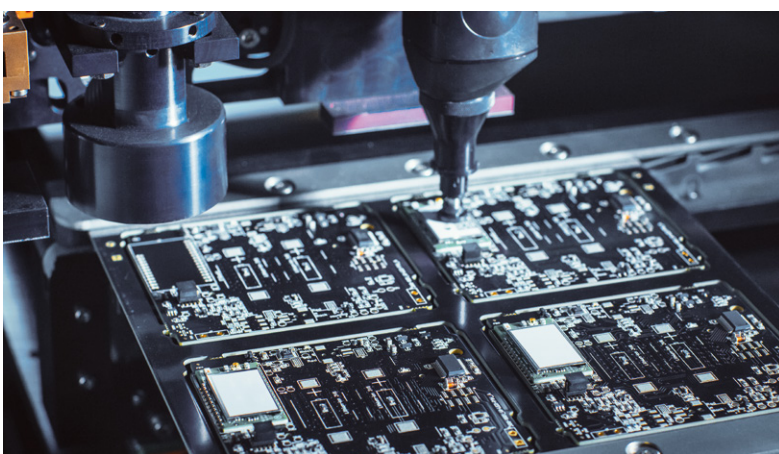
Pick-and-Place-Maschinen platzieren die Bauteile automatisch auf dem PCB.
